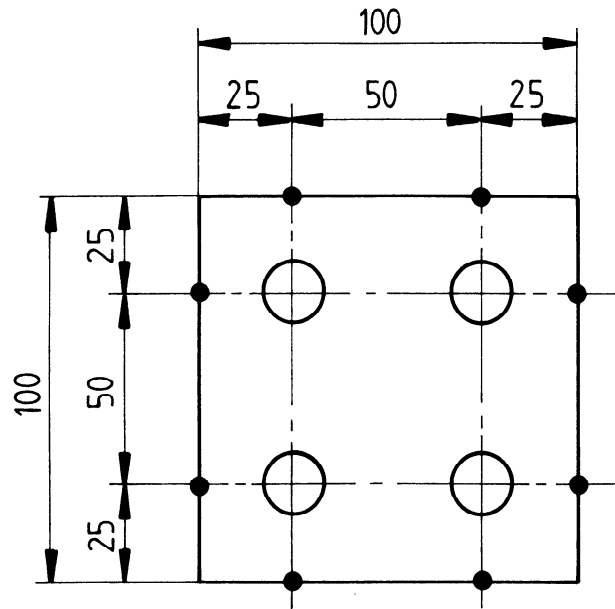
Dimensions de l'éprouvette pour les essais physiques
